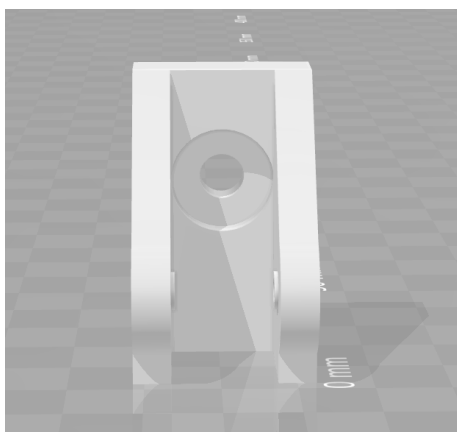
Držák motoru (1) – Autor: Rebel RepRap
